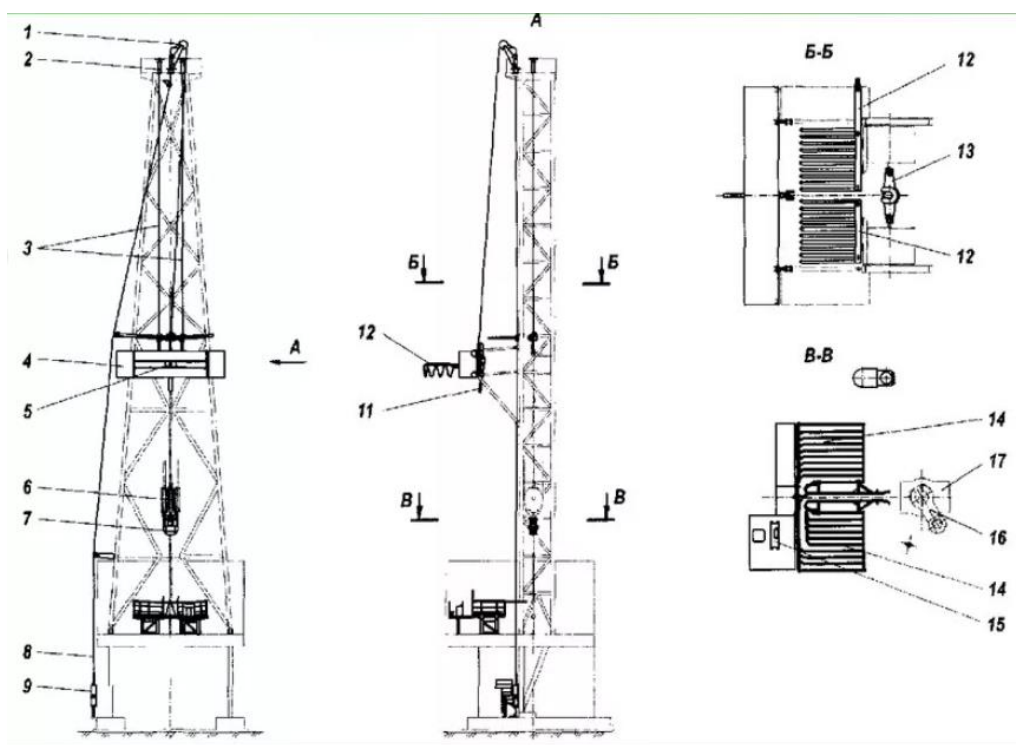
комплекс механизмов АСП: 1 – ролик обводной; 2 – амортизаторы; 3 – направляющие канаты; 4 – корпус; 5 – тележка; 6 – талевый блок; 7 – автоматический элеватор; 8 – канат подъемный; 9 – механизм подъема свечи; 11 – механизм захвата свечи; 12 – магазины; 13 – центратор подвижный; 14 – подсвечники; 15 – пульт управления; 16 – ключ АКБ; 17 – ротор с ПКР
